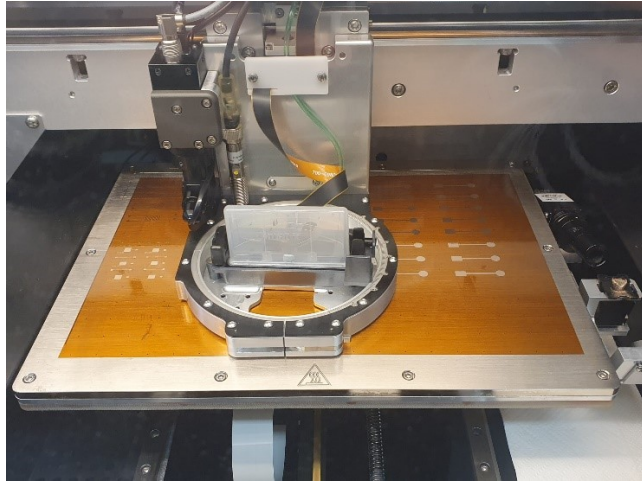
Processo di stampa della *metal pattern* del MEA.
